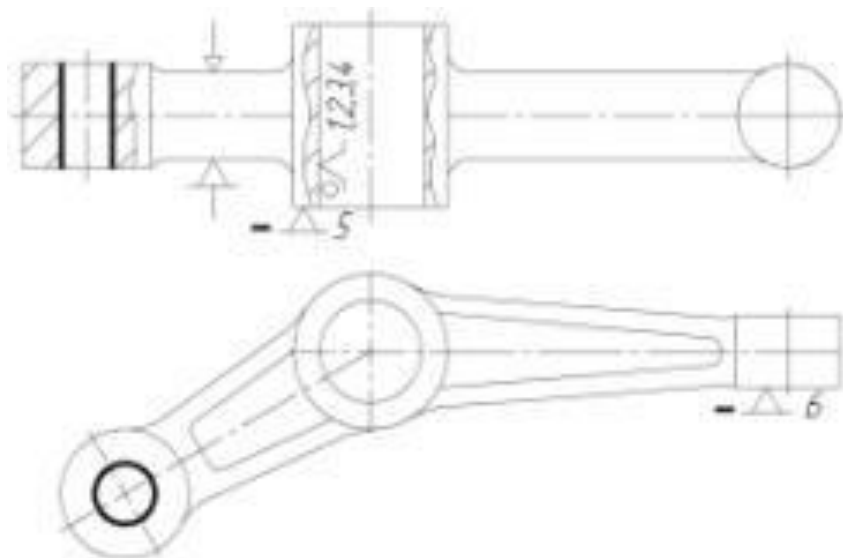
Схема базування заготовки на вертикально-свердлильній 25 операції
